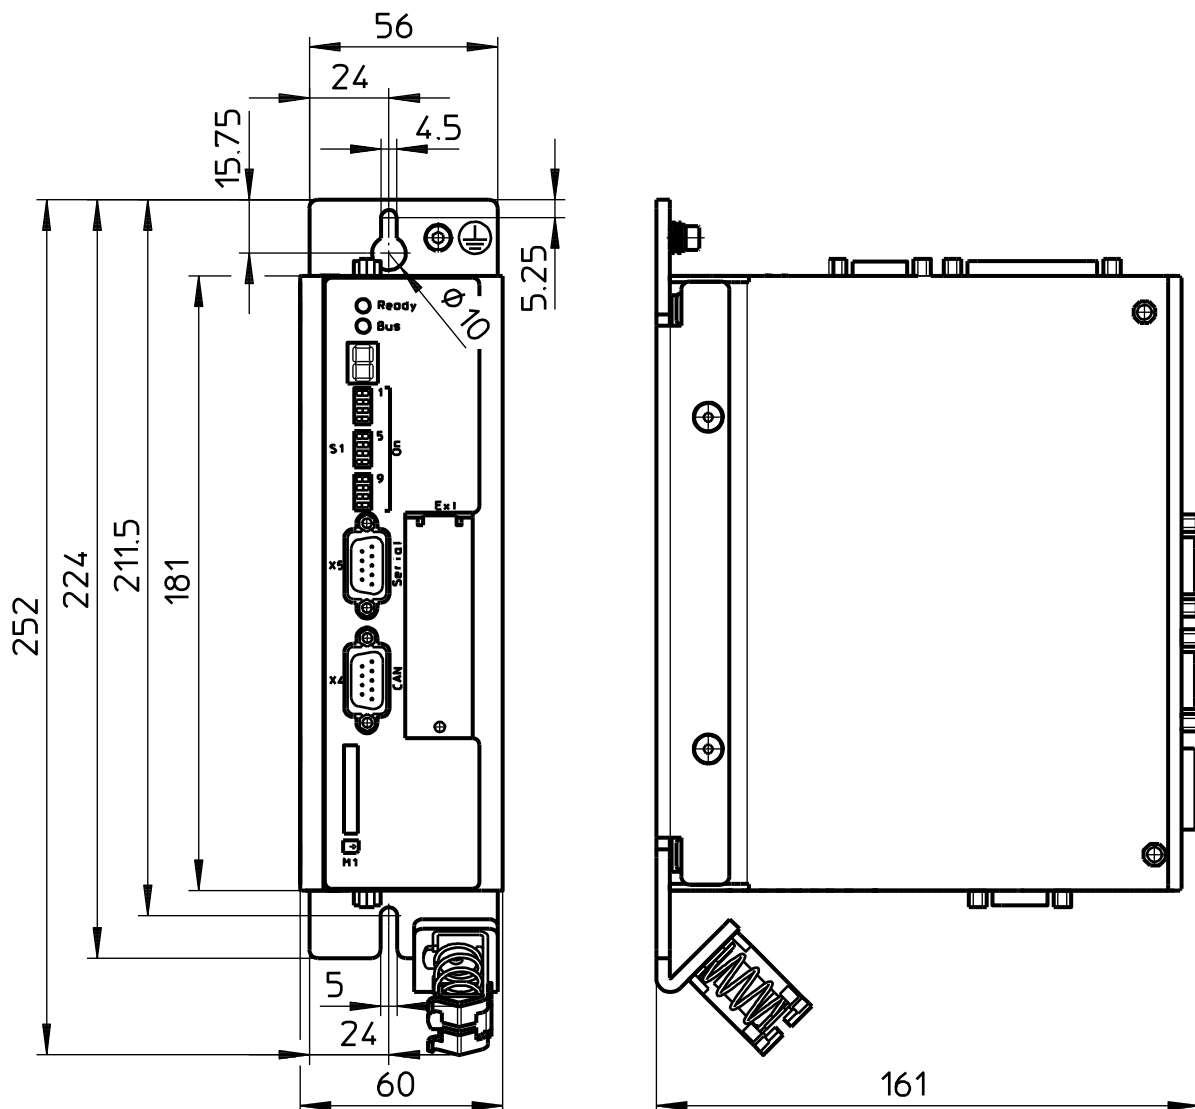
Controlador de motores paso a paso CMMS-ST: Montaje
